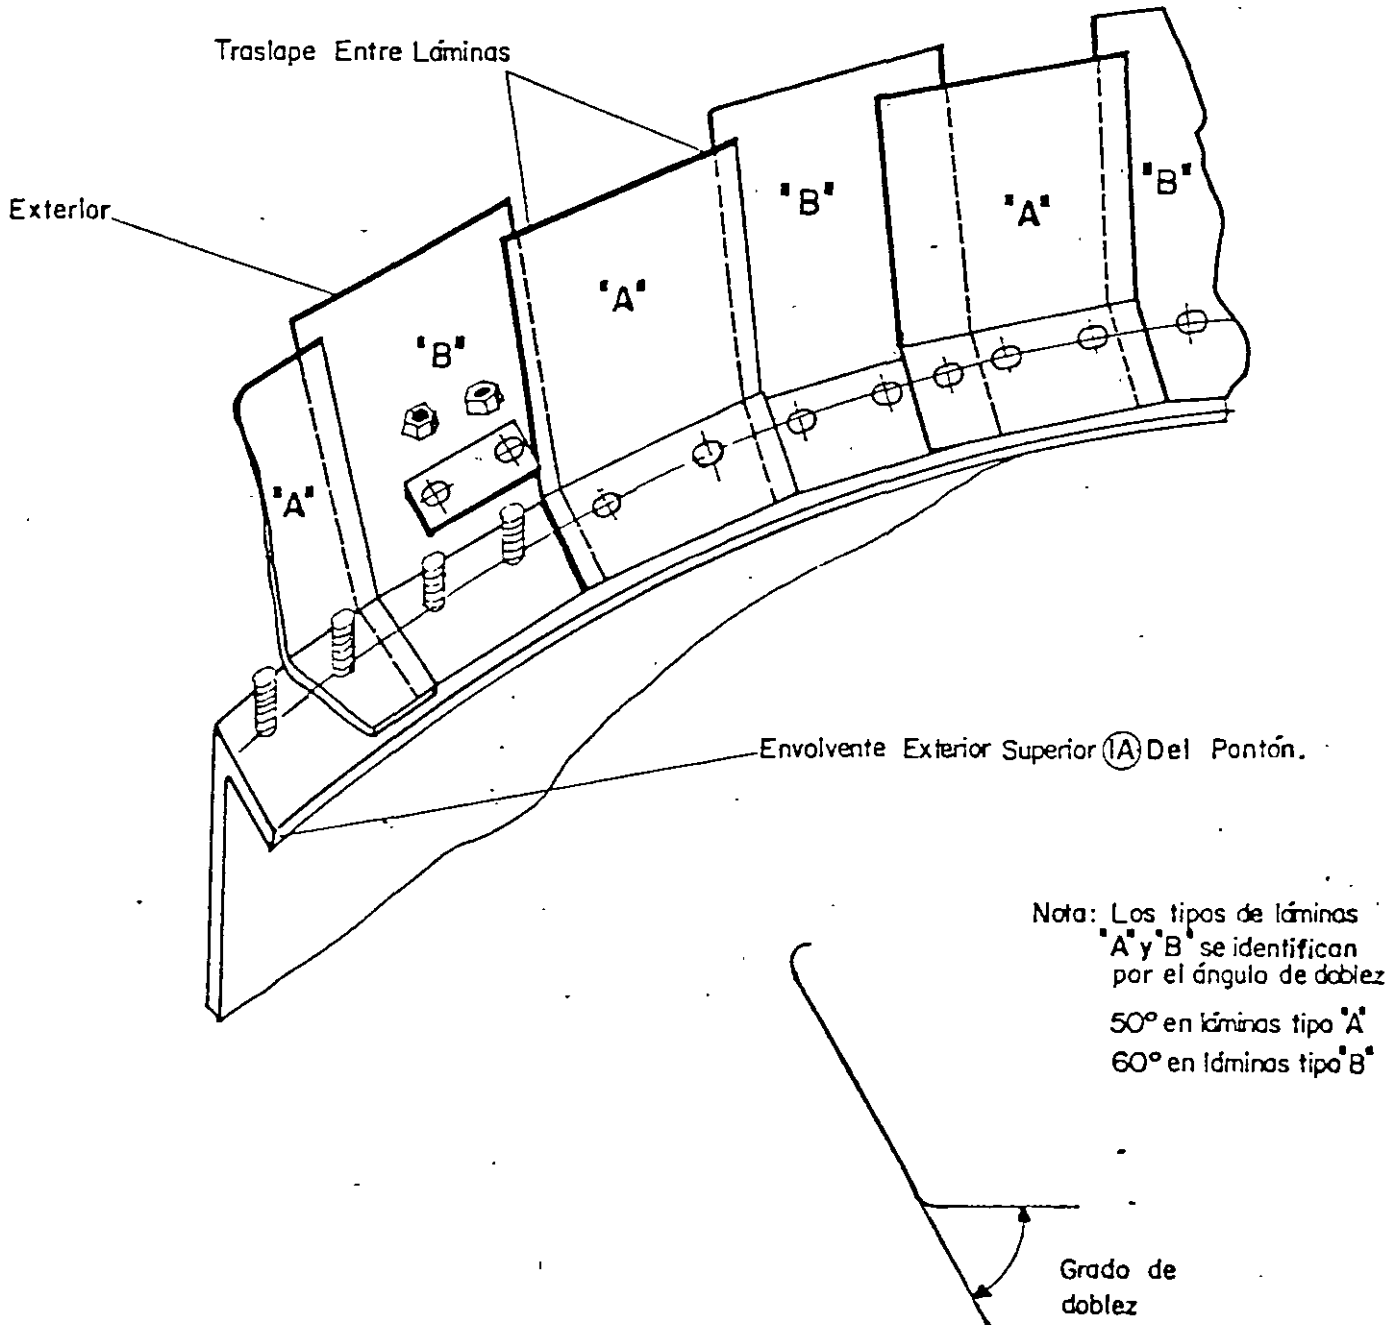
C DETALLE DE COLOCACION DE LAMINAS DE PROTECCION TIPO 'A'y'B'.
